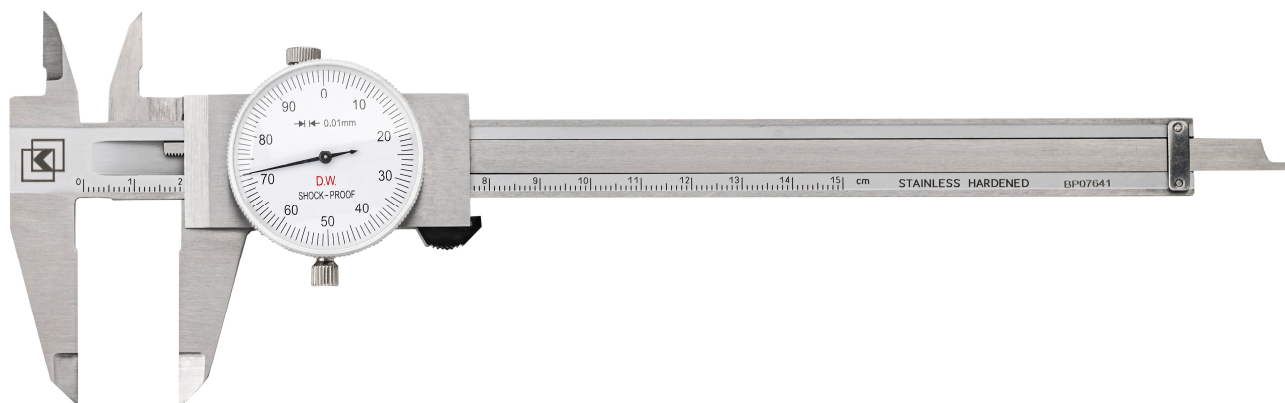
Общий вид штангенциркулей ШЦК-I
